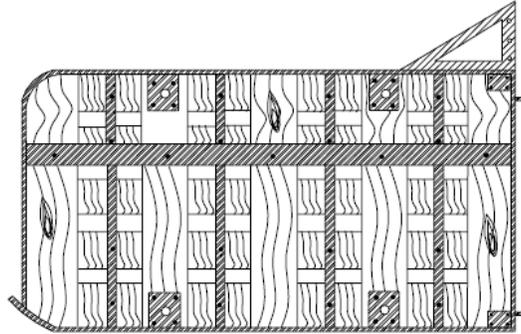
Portón rectangular plano de acero y madera para arrastre de camarón
